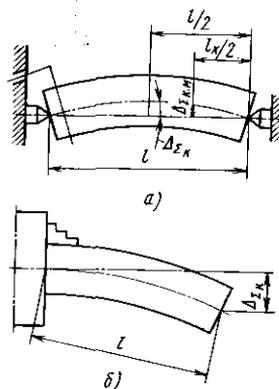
Обозначения общей и местной кривизны заготовки: а — при ее установке в центрах; б — при консольном креплении
